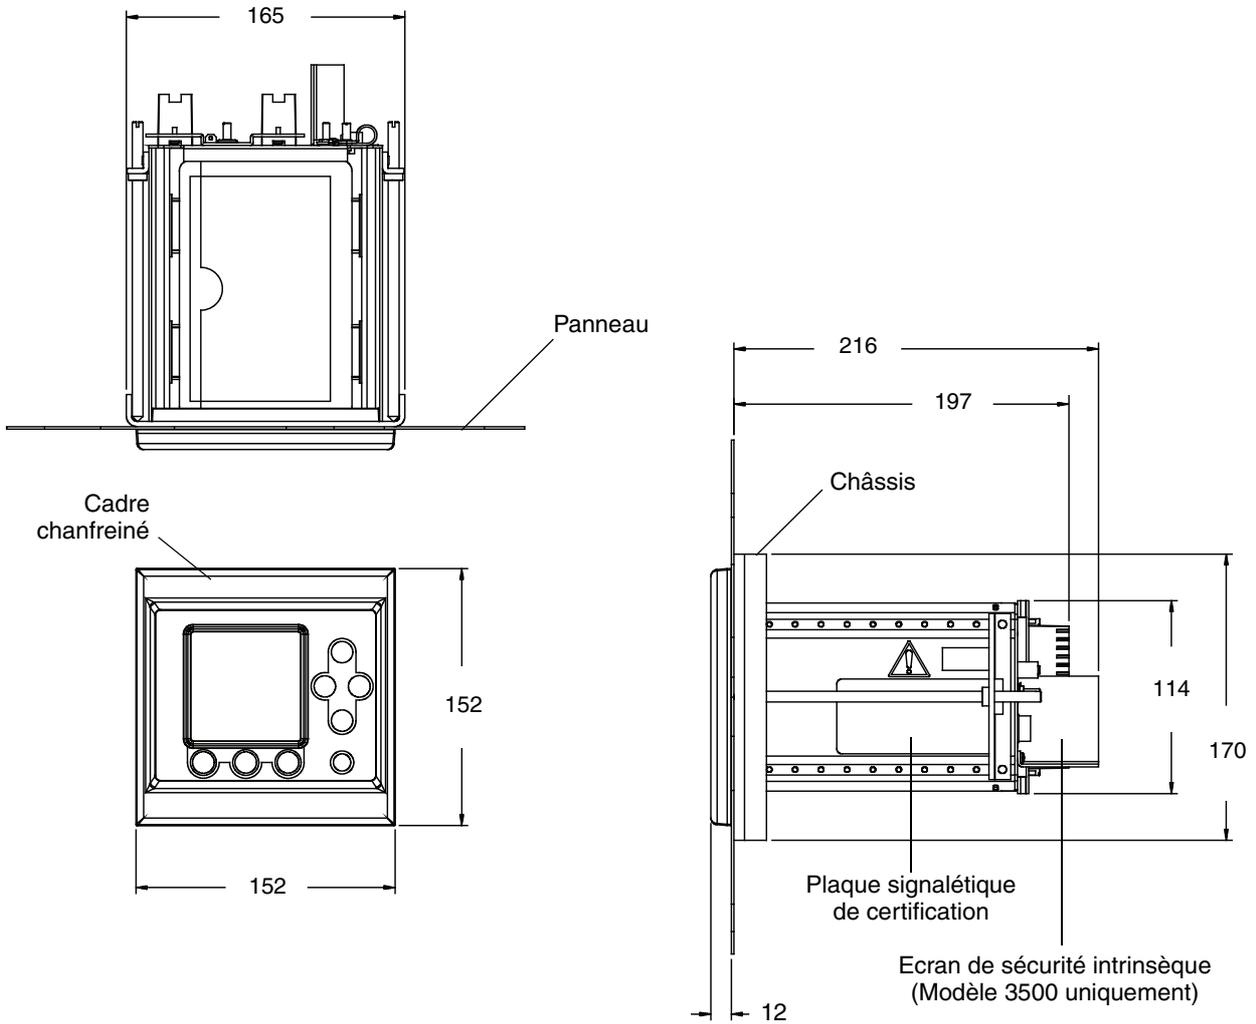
Dimensions du Modèle 3300 ou 3500 pour montage sur panneau avec câbles E/S
